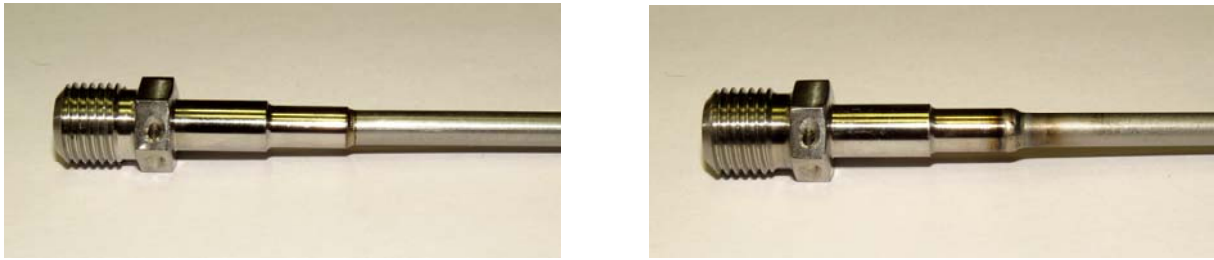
Образцы соединений тонкостенной трубы с арматурой, слева направо: лазерная сварка, импульсная автоматическая аргодуговая сварка
